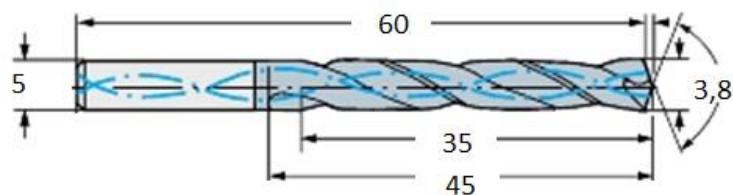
Сверло Sandvik Coromant CoroDrill 460.1-0380-029A1-ХМ GC34
